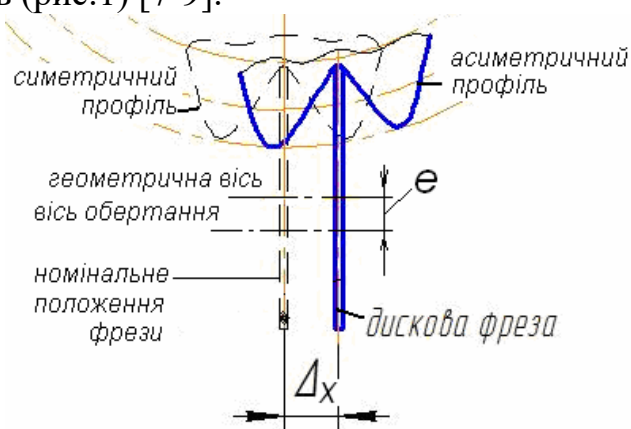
Нарізання синусоїдального колеса з асиметричними профілями зубців дисковою фрезою в умовах неперервного обкочування («радіально-коловий спосіб зубонарізання») шляхом осьового зміщення фрези
